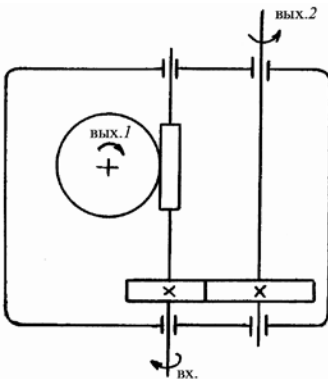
Схема двухпоточного зубчато - червячного механизма
